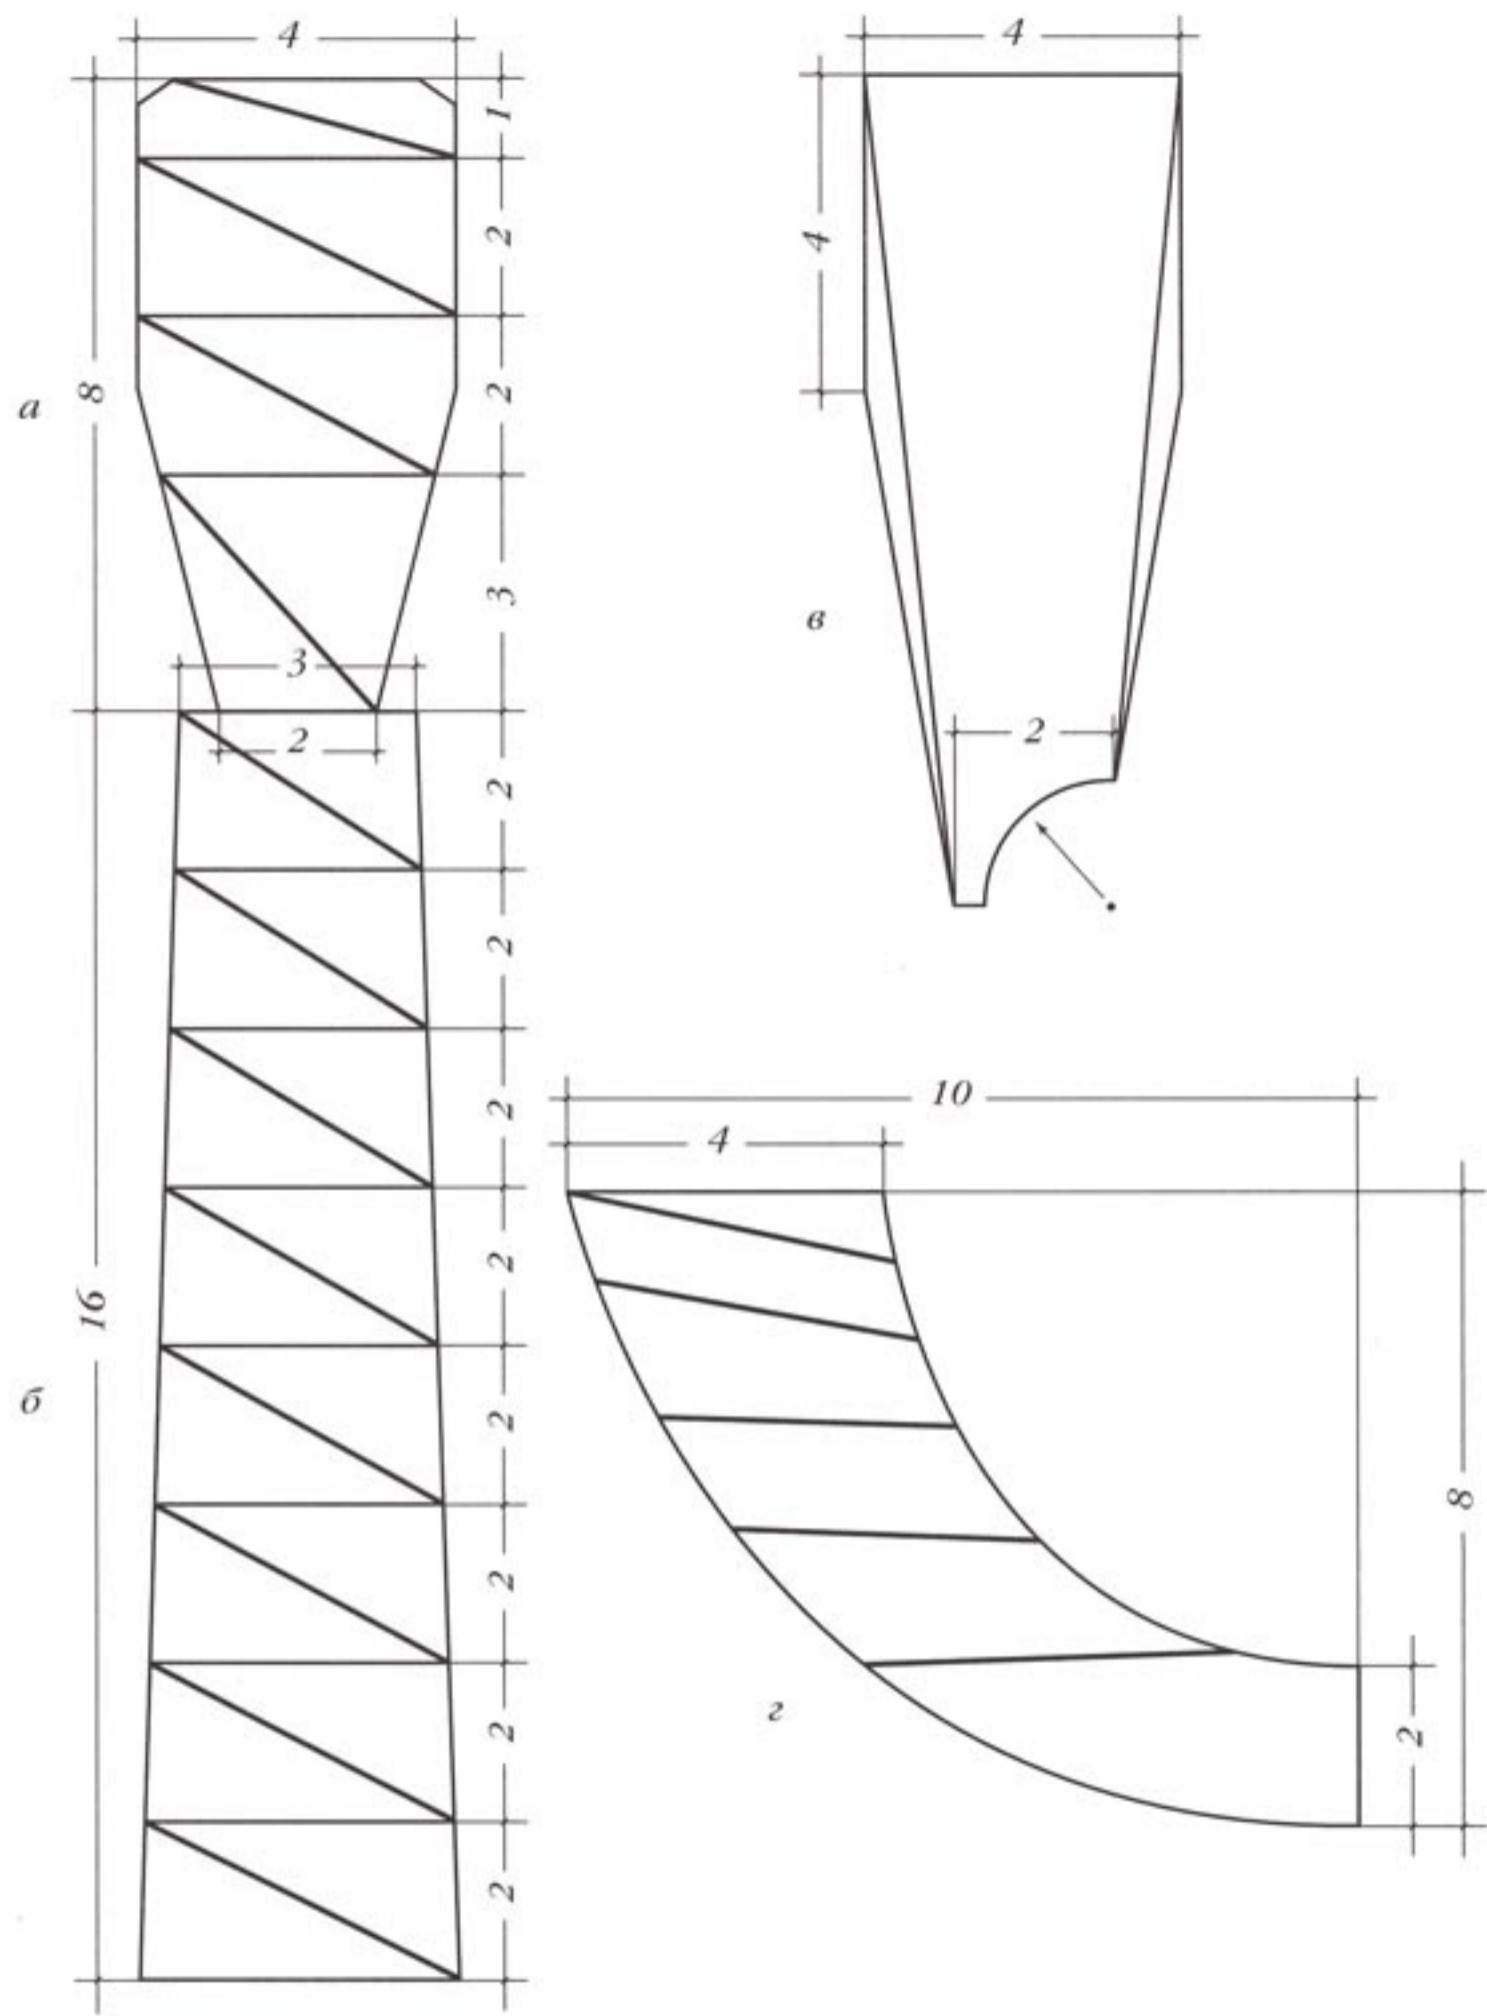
Чертеж и схема разметки стойки и рожка четырехсвечника к рис. 184: *а* – верхняя часть стойки (четырехзаходный винт); *б* – нижняя часть стойки (трехзаходный винт; шаг 2); *в* – вид рожка снизу (указан радиус места стыковки рожка со стойкой); *г* – вид рожка сбоку
